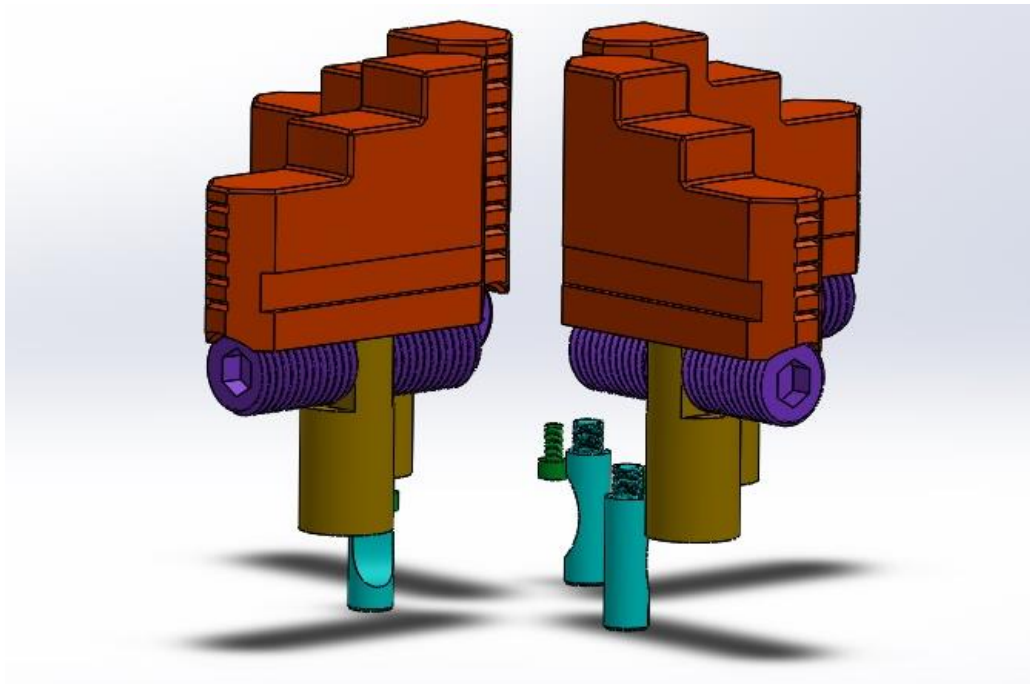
Ensamblaje sin plato en Solidworks 2017
